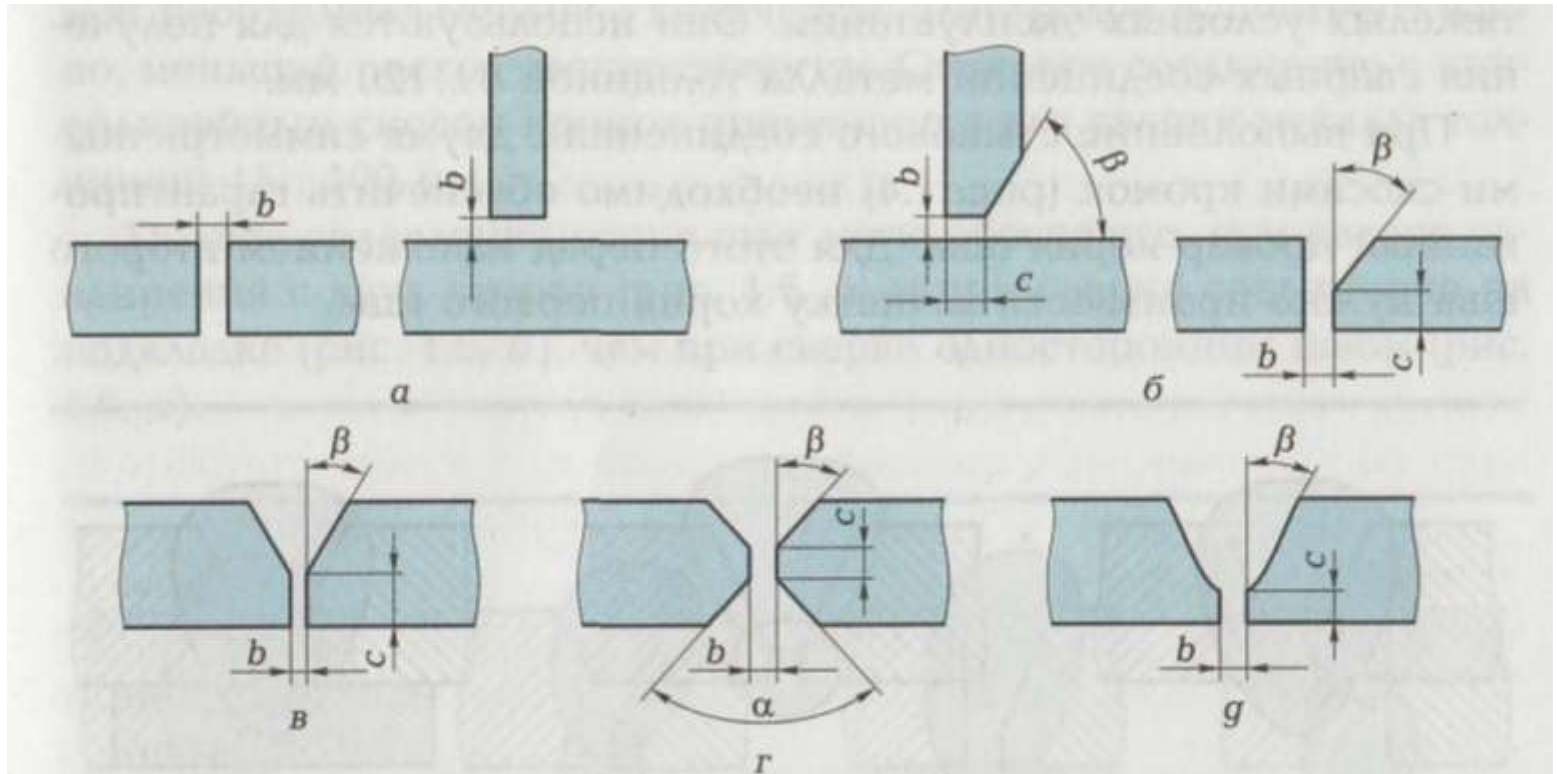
Конструктивные элементы разделки кромок под сварку:
